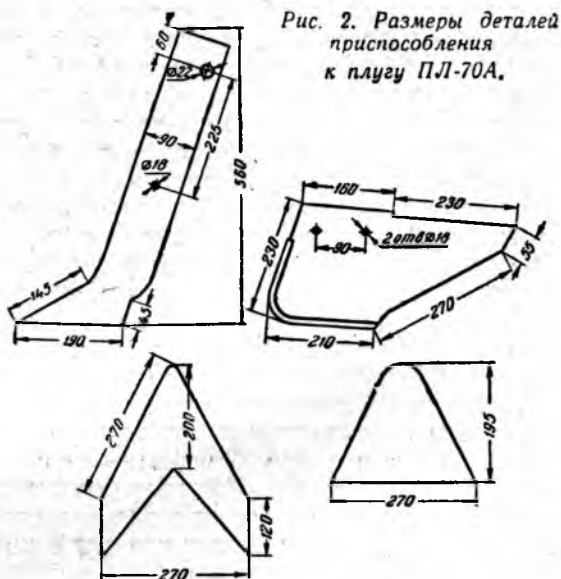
Размеры деталей приспособления к плугу ПЛ-70А.
